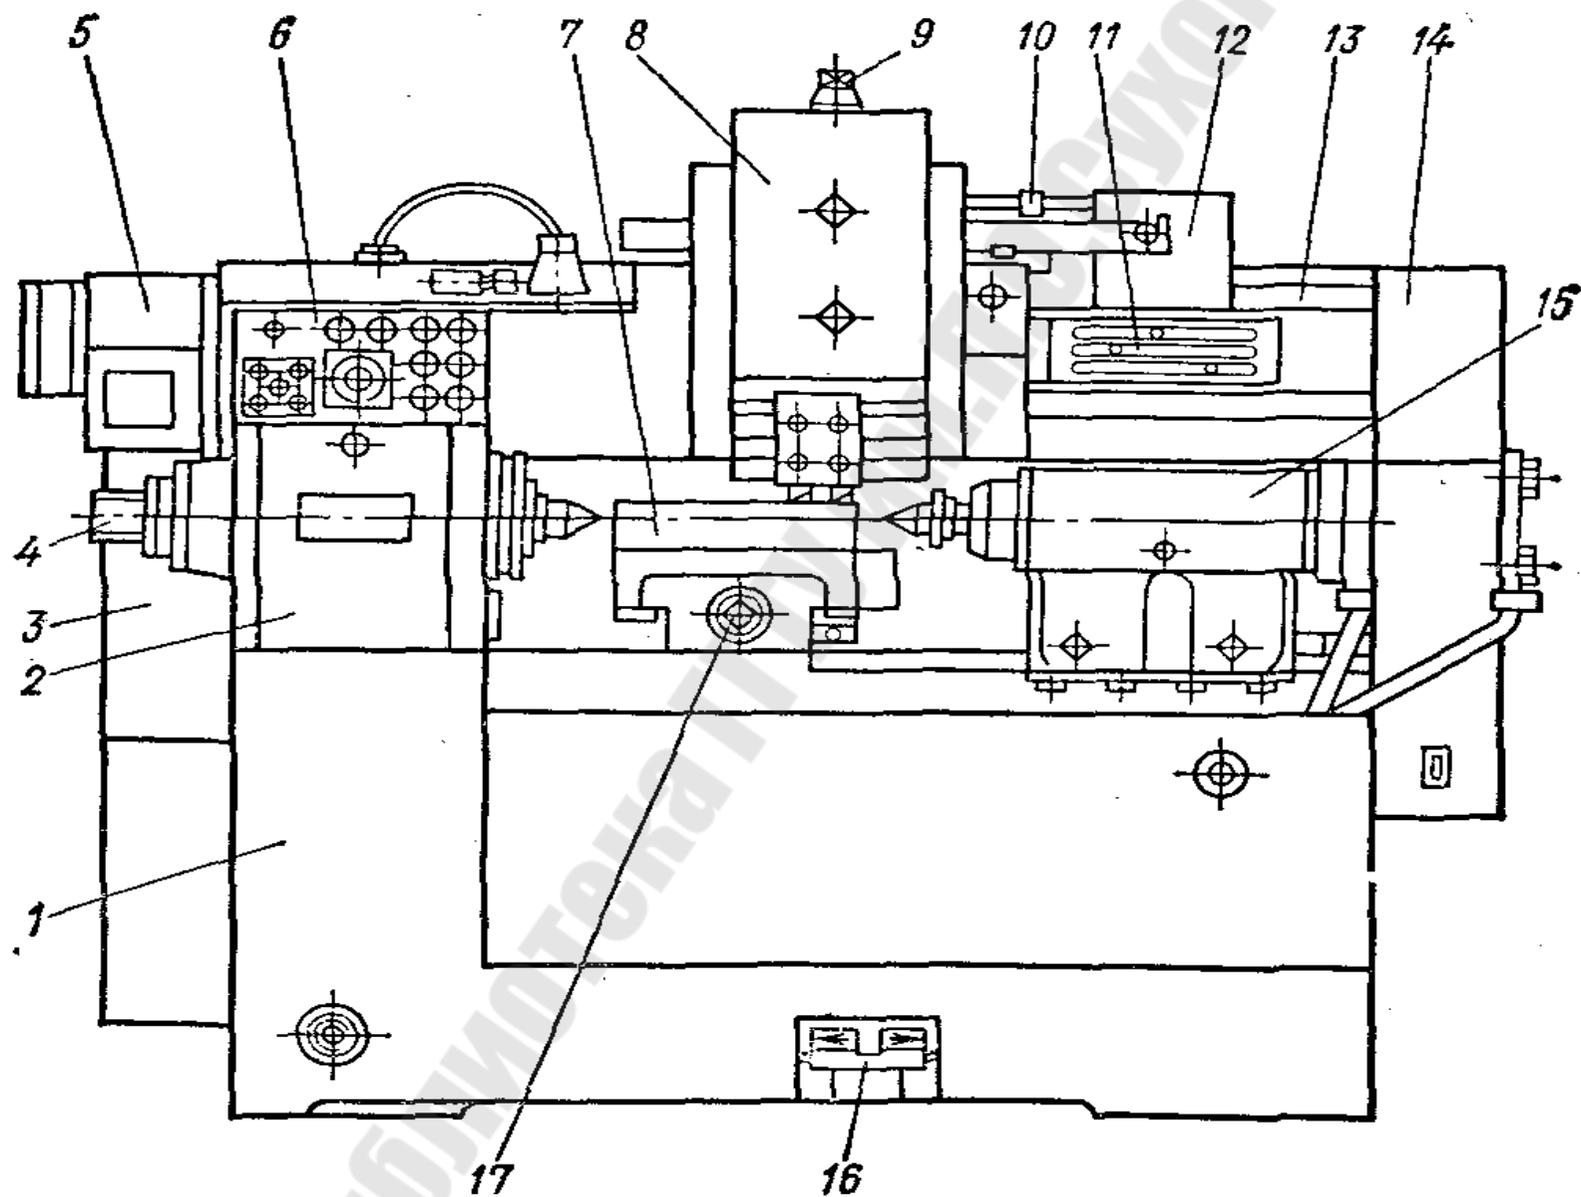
Общий вид токарного многорезцового полуавтомата
